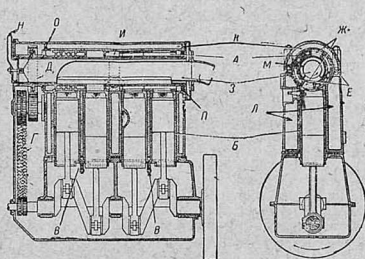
Продольный и поперечный разрезы двигателя Мак-Ларен с вращающимися клапанами
